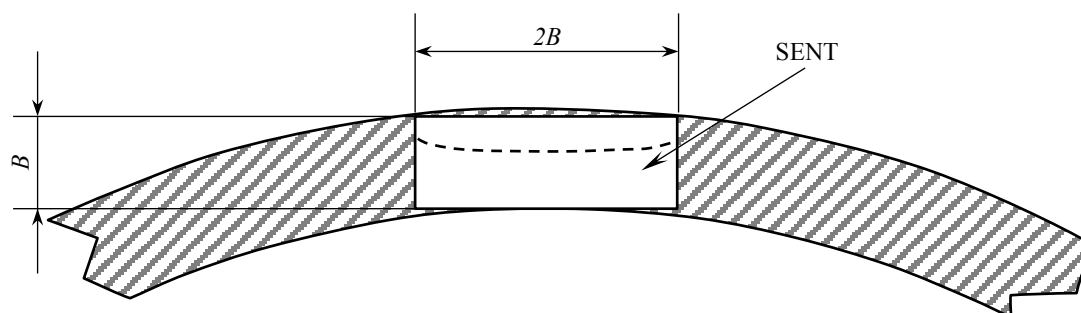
Поперечное сечение образца SENT из кольцевого сварного соединения трубы
